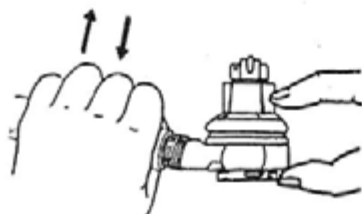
Проверка люфта в шарнирах рулевых тяг
